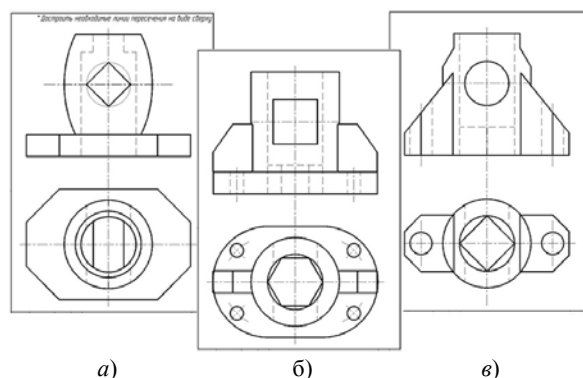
Пример заданий, созданных генератором из базовых элементов форм деталей: *a* — базовый корпус – тор, фланец – призма; *b* — базовый корпус – цилиндр, фланец комбинированный; *v* — базовый корпус комбинированный
